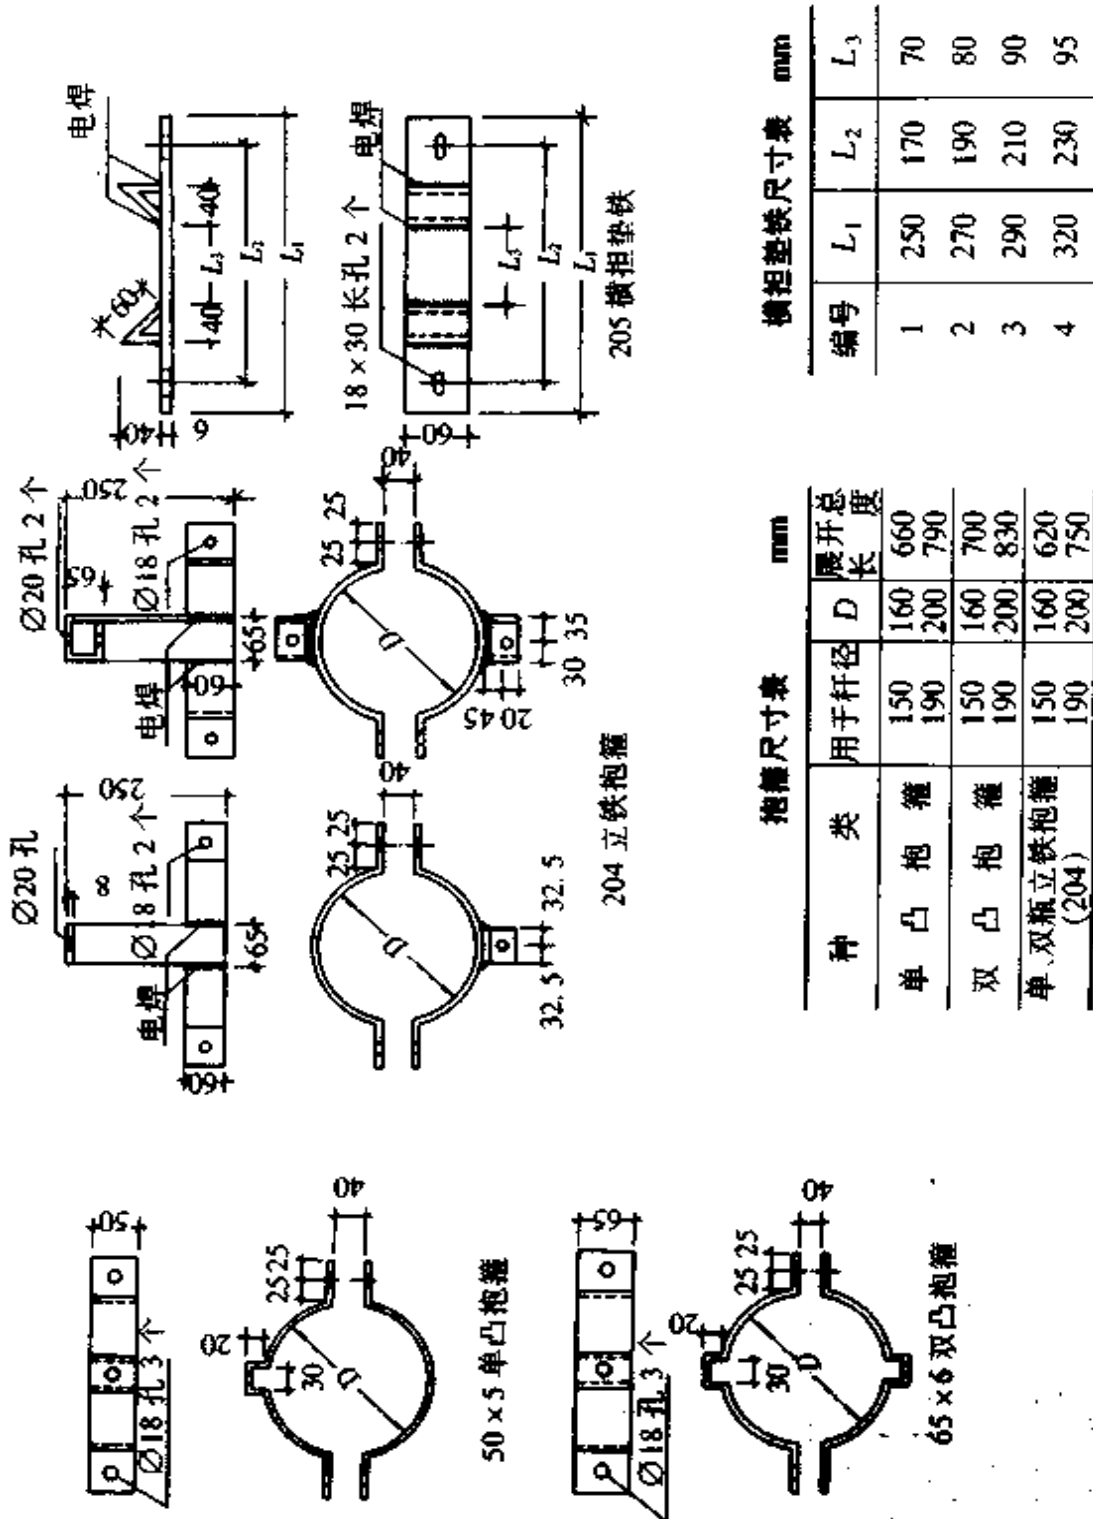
钢筋混凝土电杆附件加工图(四)
